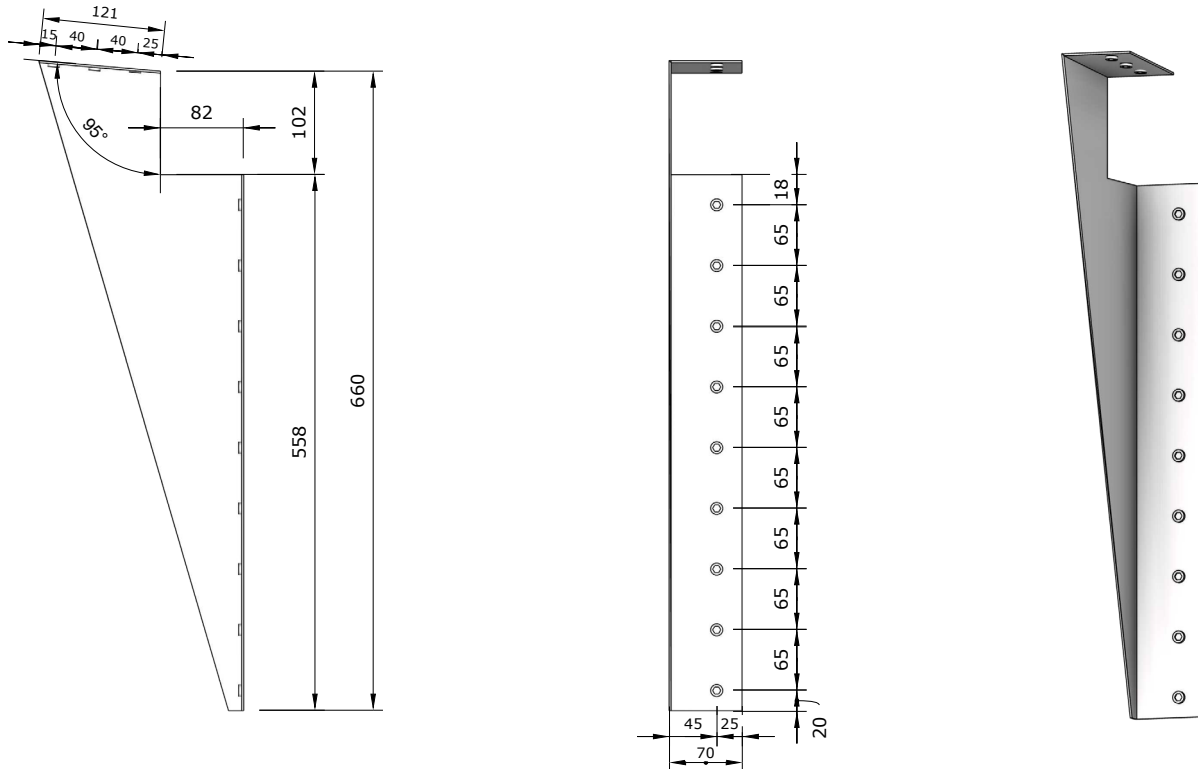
Ansichten des Stützbleches mit der Vermassung der Befestigung, Masse in mm.
